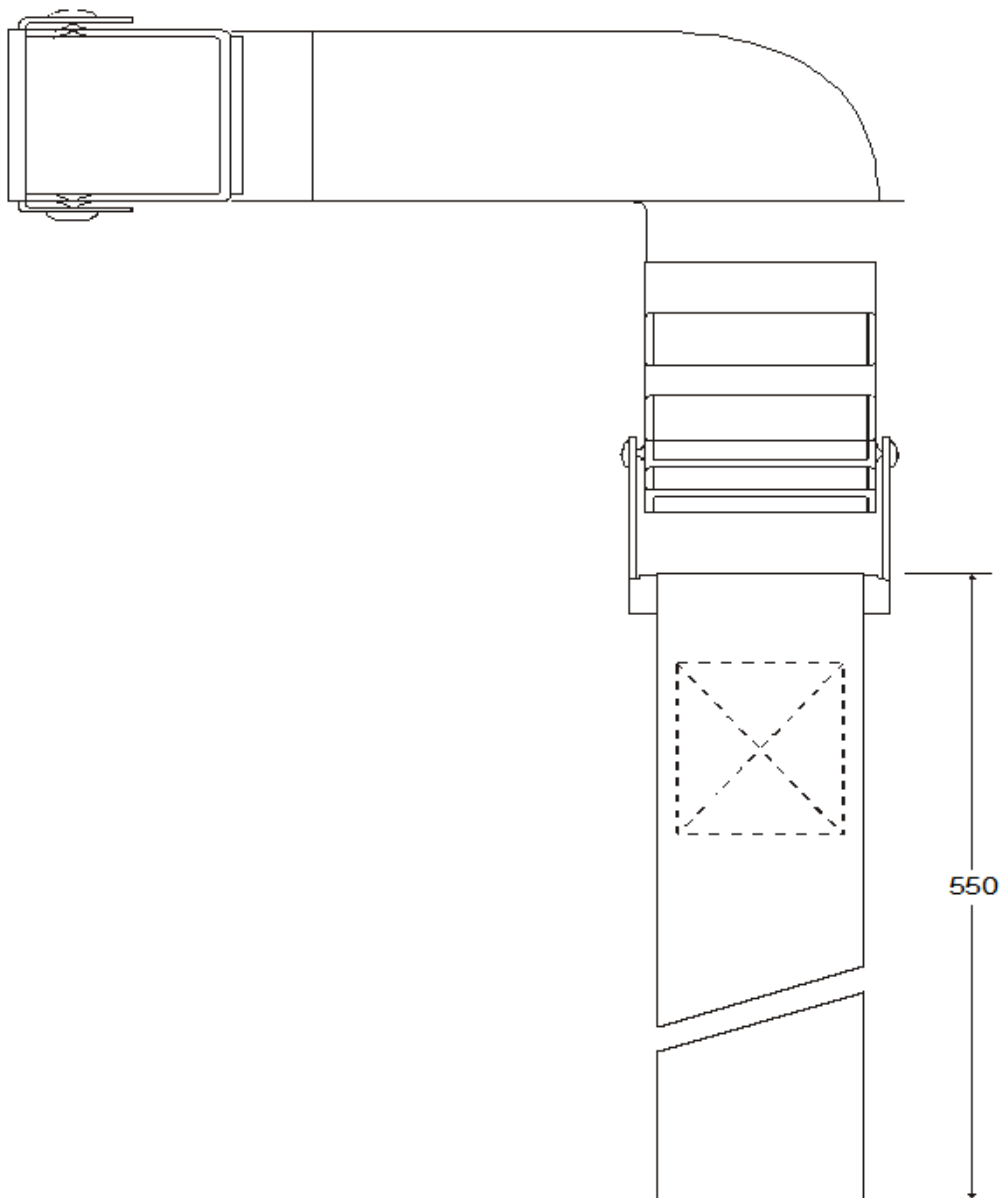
Vista da correia de fixação do suporte metálico (medidas em mm)
